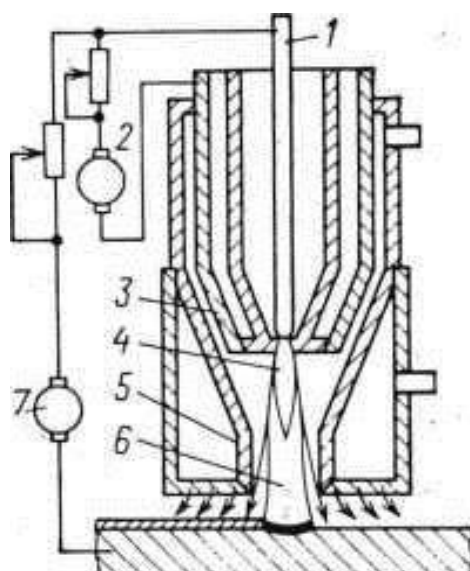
Схема плазменной наплавки с вдуванием порошка в дугу:
